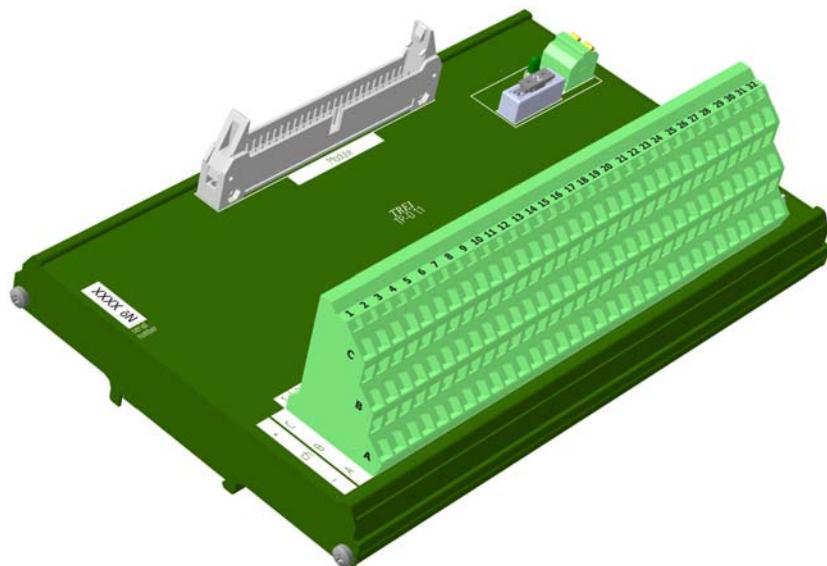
Чертеж общего вида ТР-2VIso с указанием габаритных размеров
